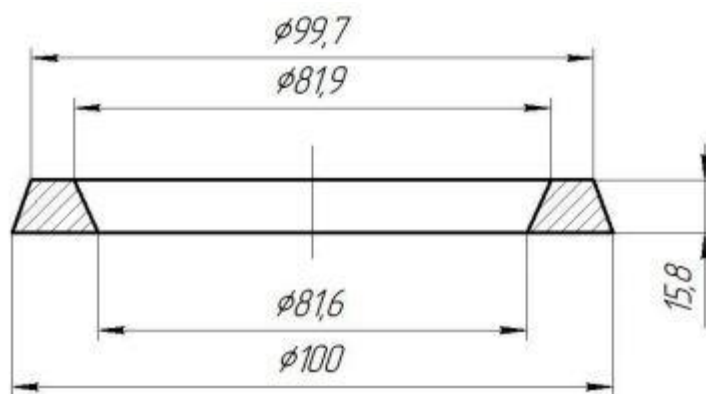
Эскиз опытной детали для определения величины увода струи гидроабразивного станка Idroline 1740
